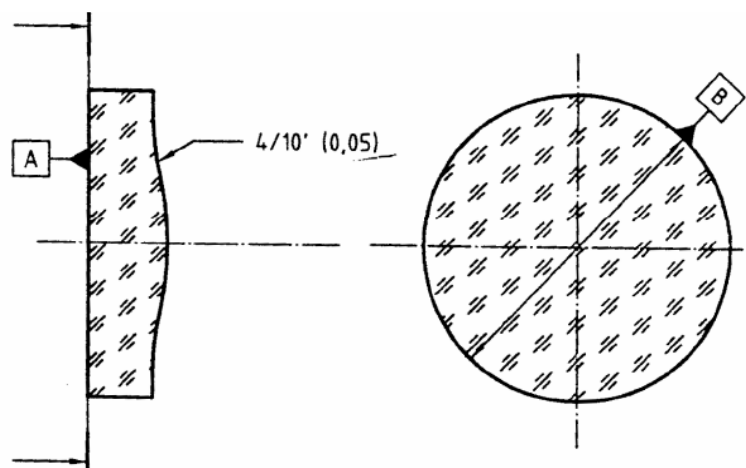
Допуск на центрування асферичної поверхні
